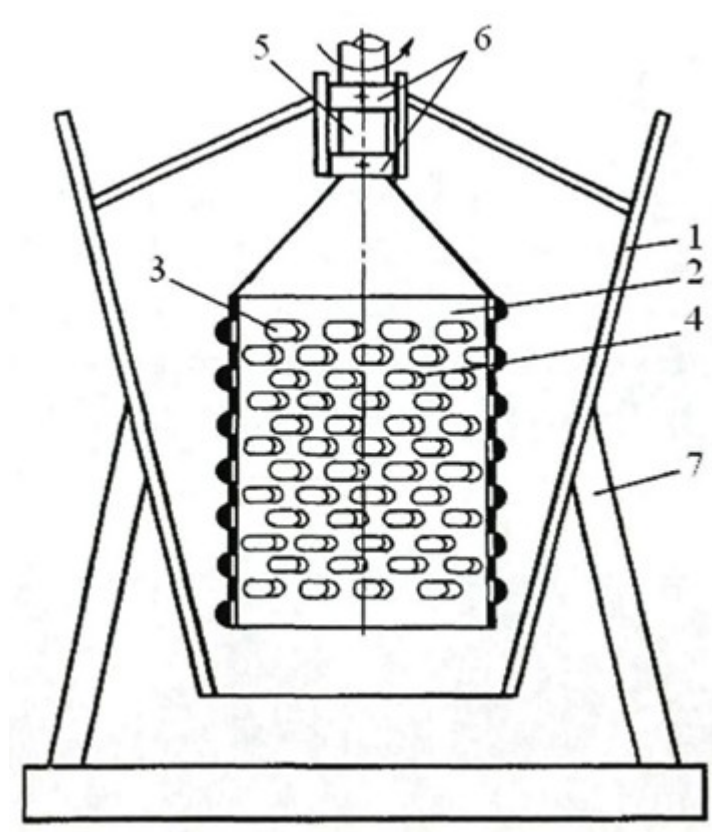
Вертикальний барабанний подрібнювач
